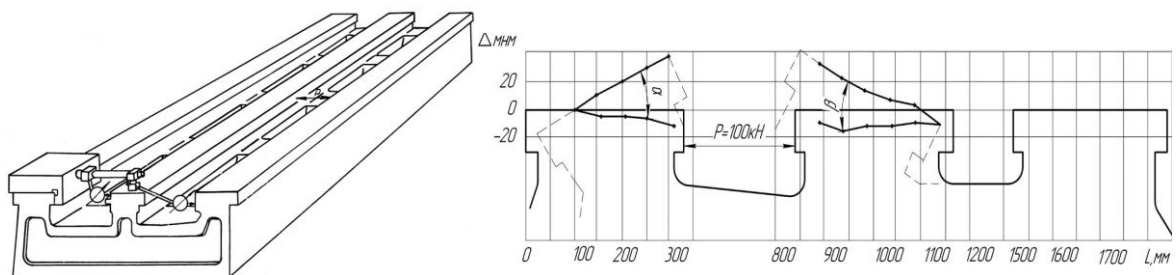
Схема вимірювання деформації при розтиску полиць литої станини верстата 1А665 за допомогою індикатора
